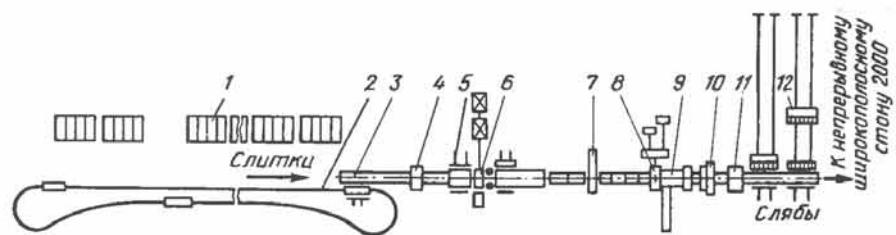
Схема расположения оборудования слябинга 1250:1 – нагревательные колодцы; 2 – кольцевая слиткоподача; 3 – приемный ролганг; 4 – весы; 5 – манипулятор; 6 – универсальная рабочая клеть; 7 – МОЗ; 8 – ножницы; 9 – конвейер уборки обрезков; 10 – клеймовочная машина; 11 – весы для слабов; 12 – устройство для уборки слабов
